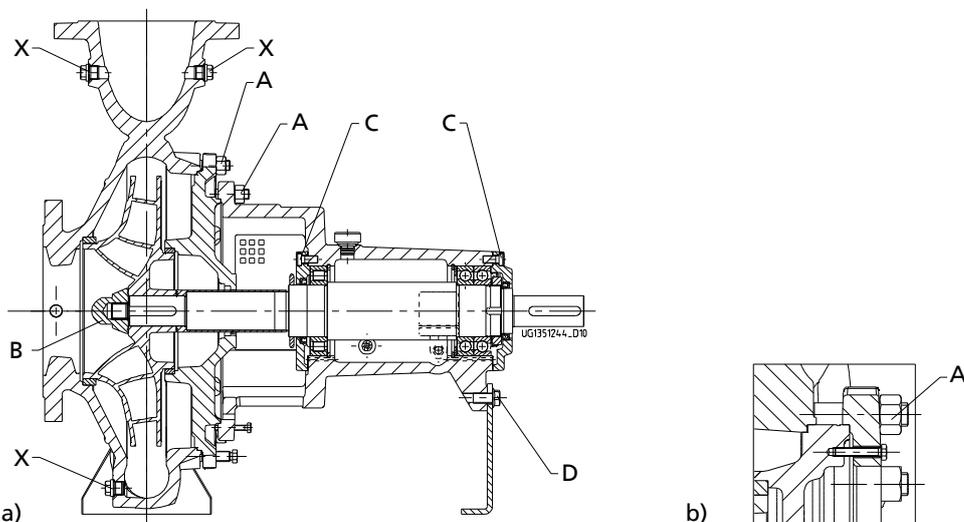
a) Punti di serraggio della pompa, b) Versione con coperchio del corpo bloccato
